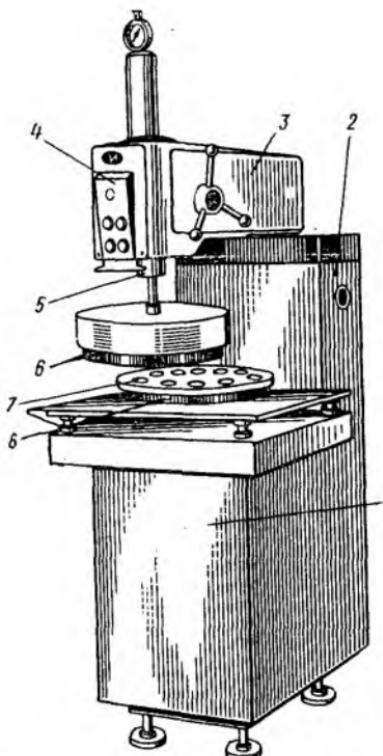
Двухдисковый вертикально-доводочный станок 3Б814:
